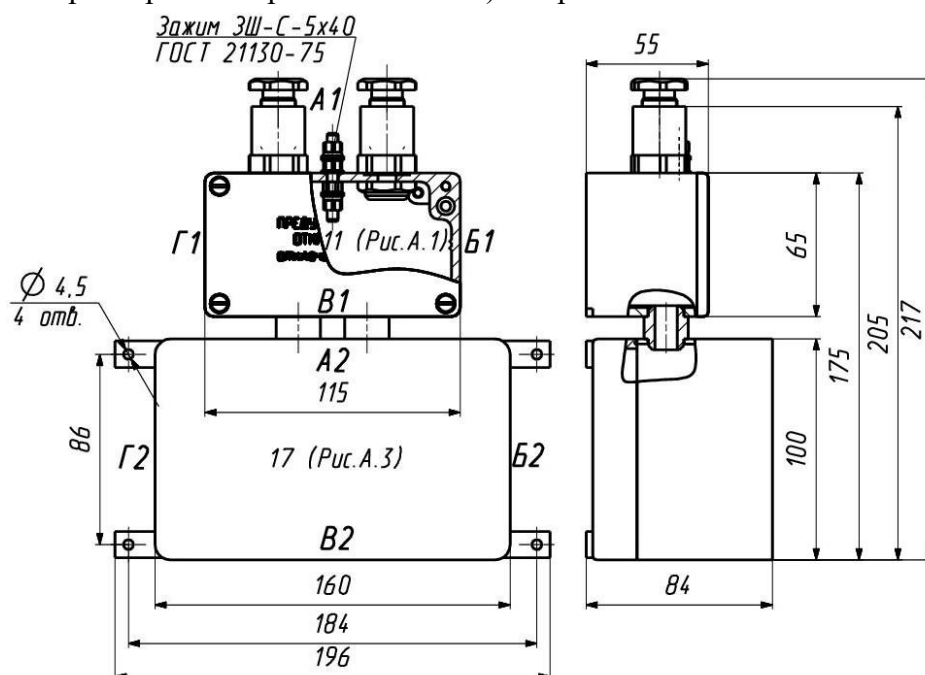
Блок корпусов и коробка клеммная ЕхБКР-А11В1/А17А2 (скрепление корпусов типоразмеров 11 и 17 сторонами В1 и А2) – вариант 8
